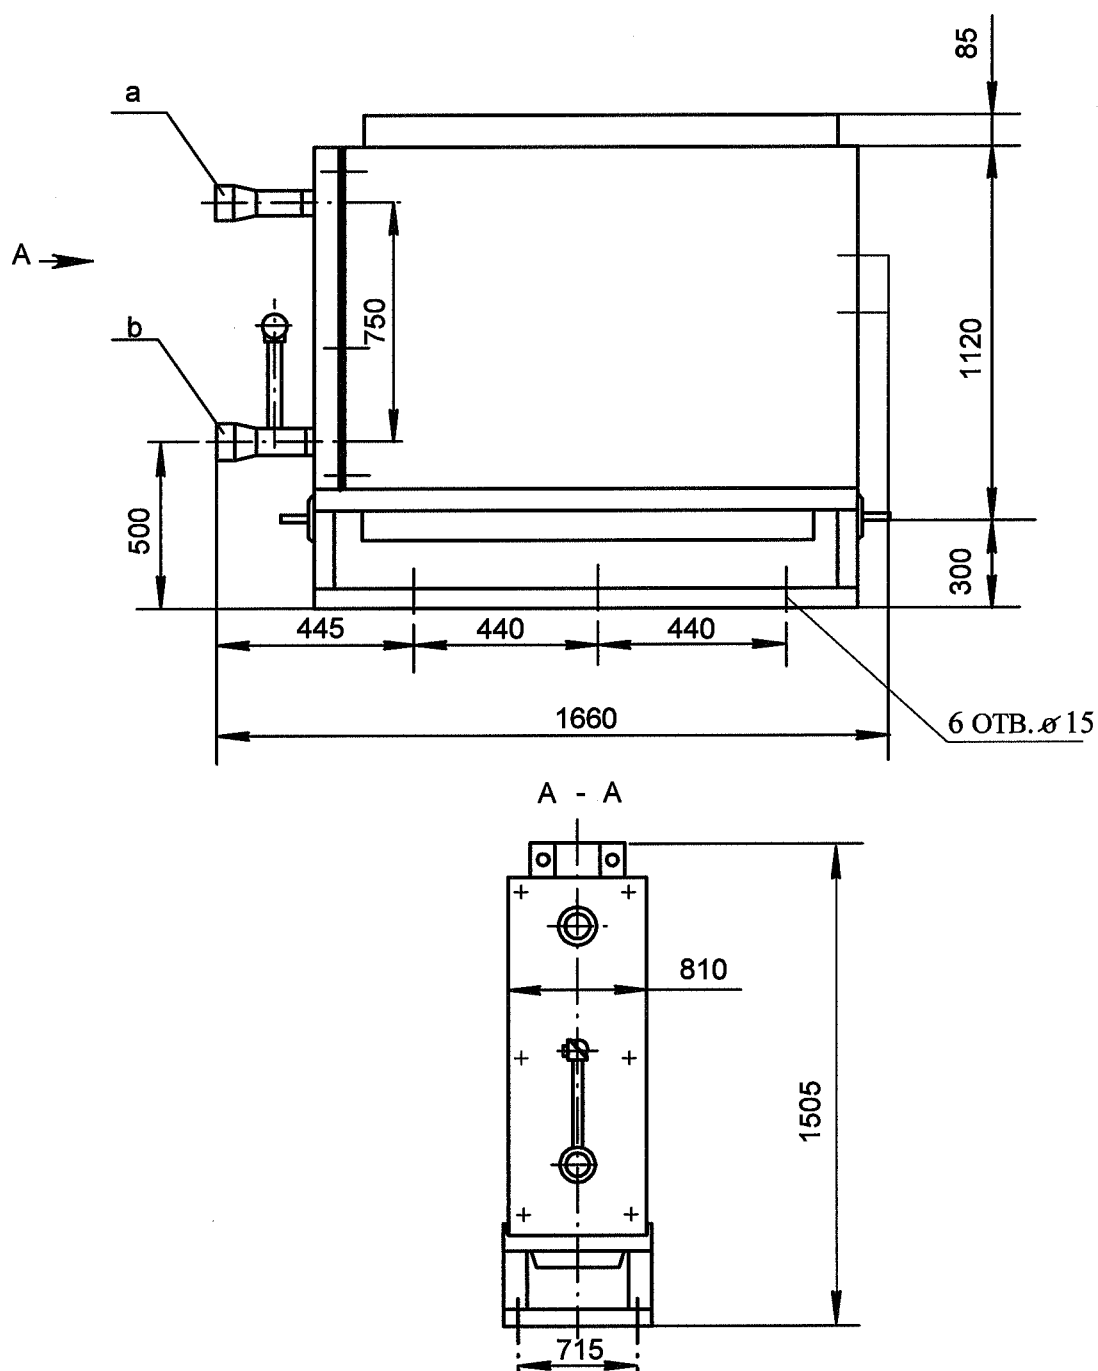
Габаритный чертеж электронагревателя KPL11AH001, KPL12AH001
